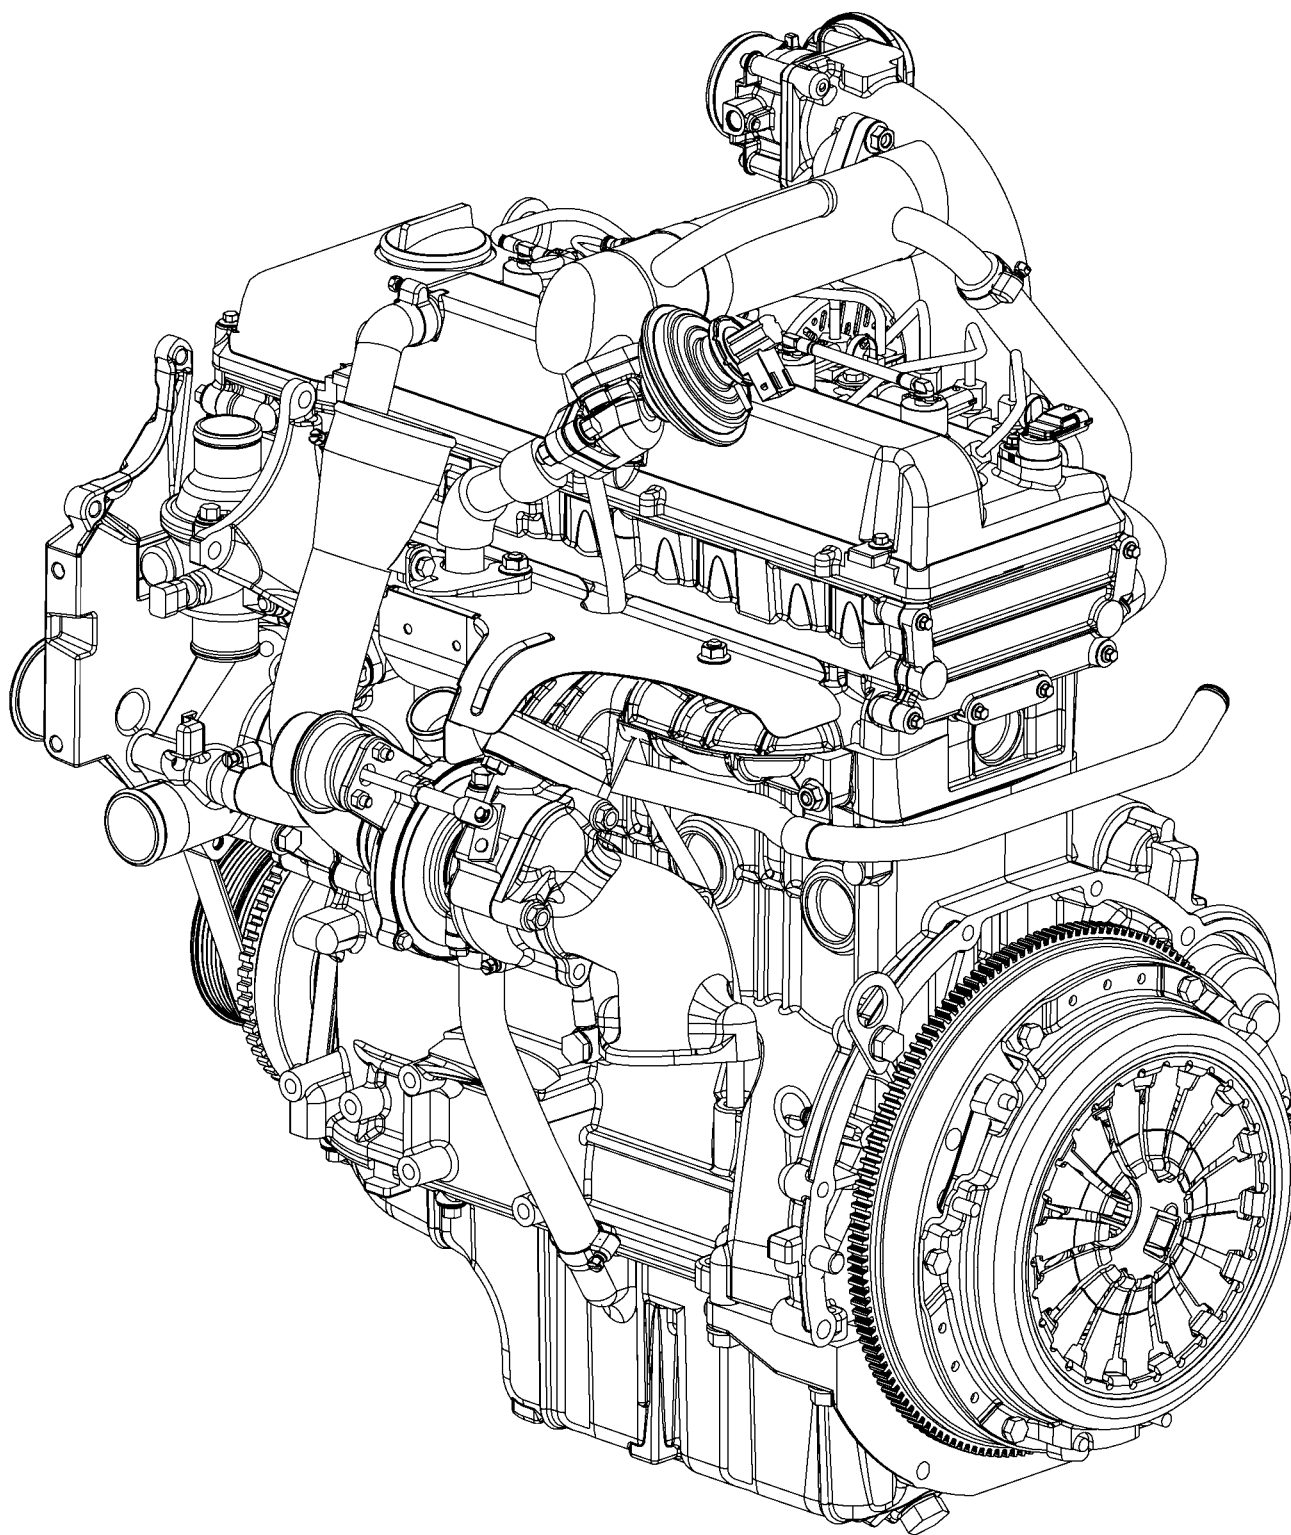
Внешний вид двигателя без компрессора кондиционера, насоса ГУР и деталей привода вентилятора
